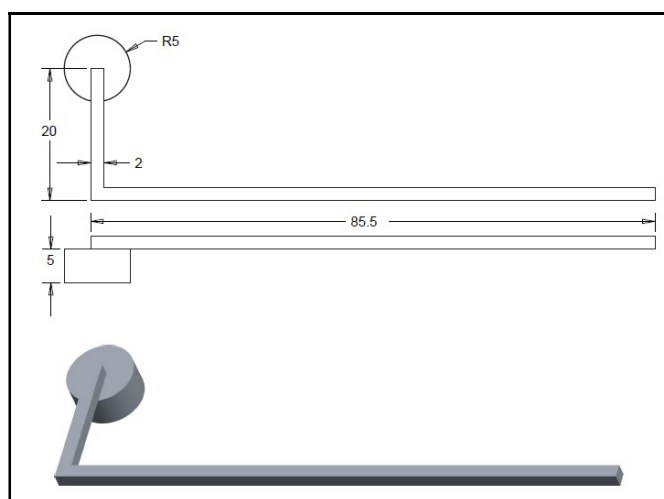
Desenho técnico do teste cilíndrico com o detalhe da barra dimensionada.
